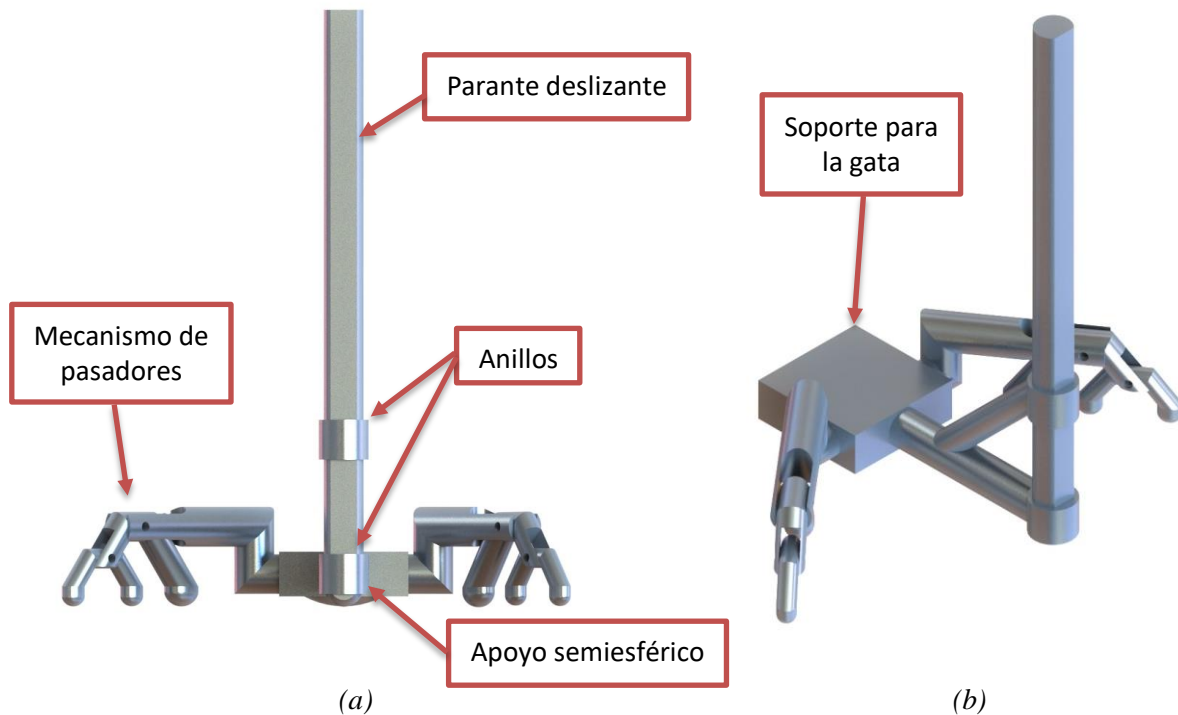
Vistas de la posible solución base 1, (a) vista frontal, (b) vista isométrica
